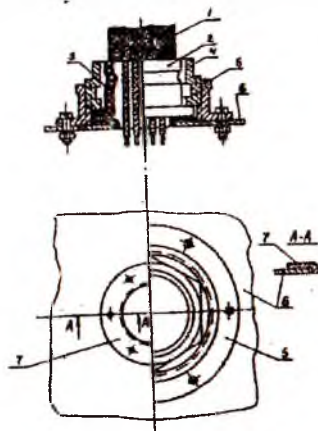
Кабельный ввод в корпус из алюминиевого сплава:
